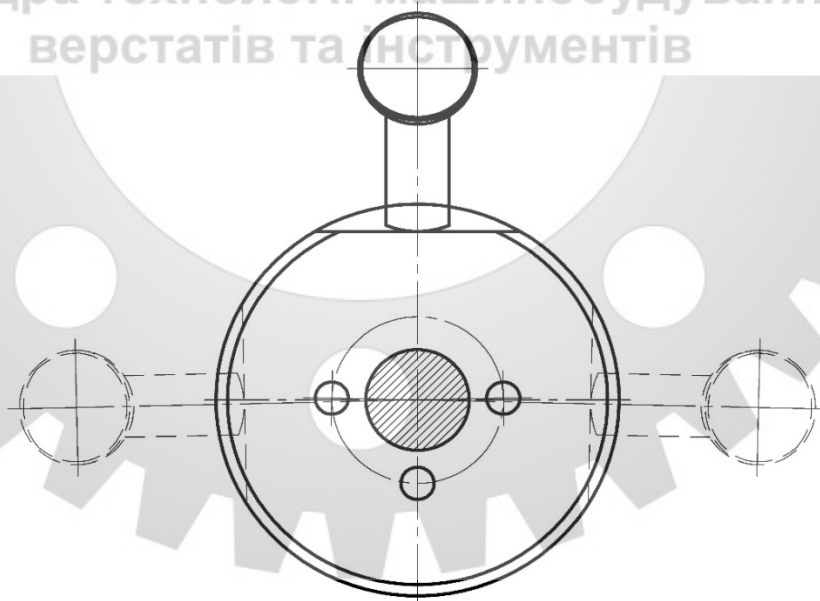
Положення рукоятки переключення блоків коробки швидкостей з трьома зубчатыми колесами
